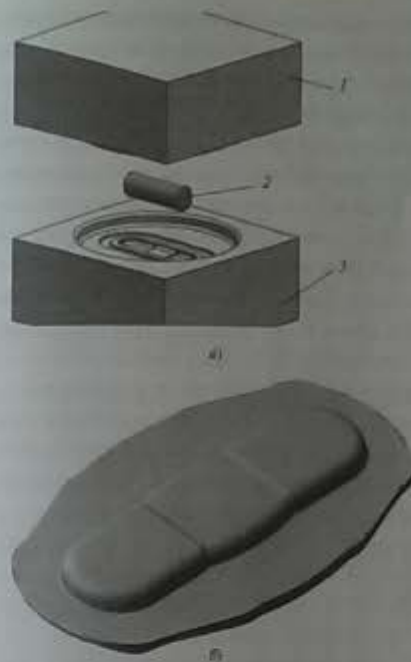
Открытый штамп с заготовкой (а) и модель поковки, полученной в открытом штампе (б): 1 — туансон; 2 — заготовка; 3 — матрица
